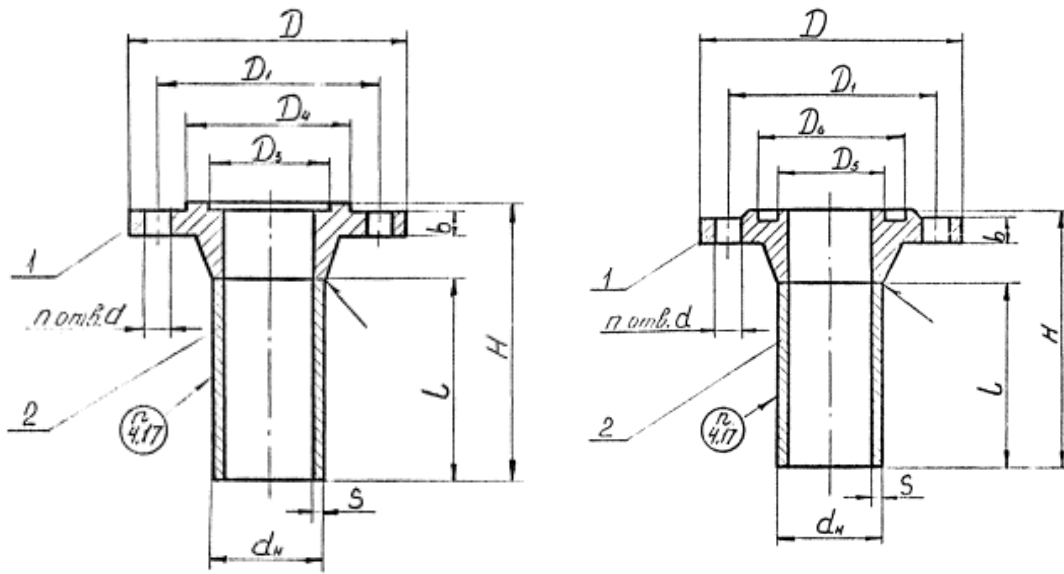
Штуцера с фланцами приваренными встык с уплотнительной поверхностью типа шип-паз на условное давление 4,0 МПа
